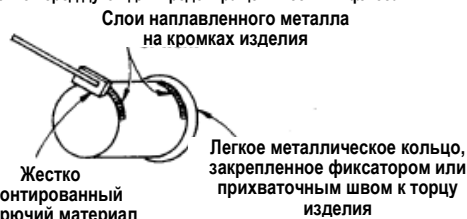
Для обеспечения сварки около кромок им требуются устройства для удержания флюса.
